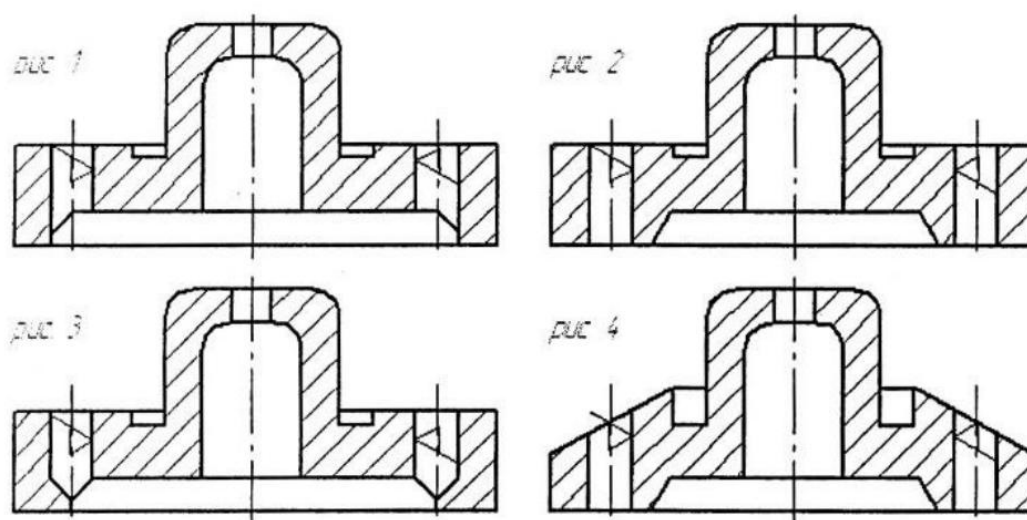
Примеры правильной и неправильной конструкции детали для обработки отверстий
